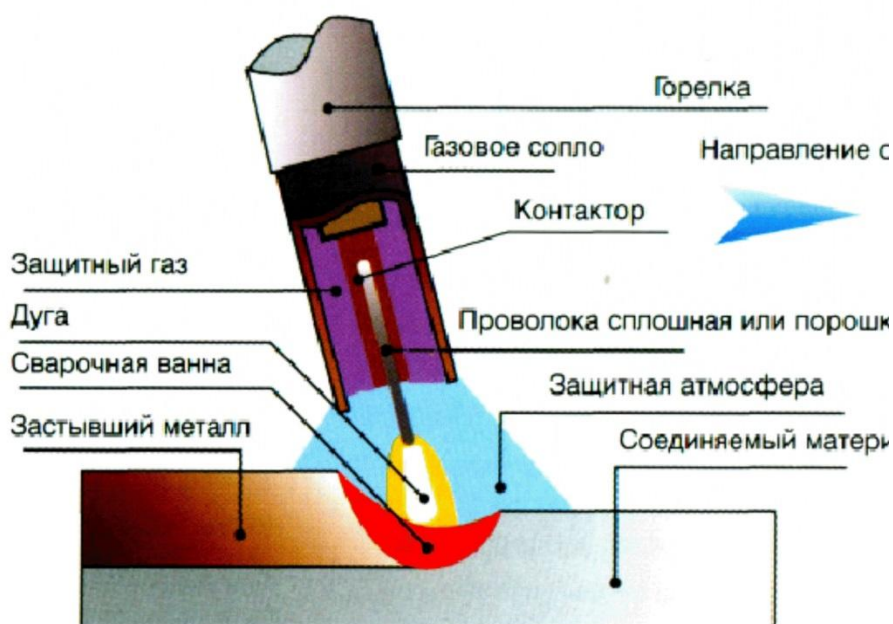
Схема механизированной сварки в углекислом газе
